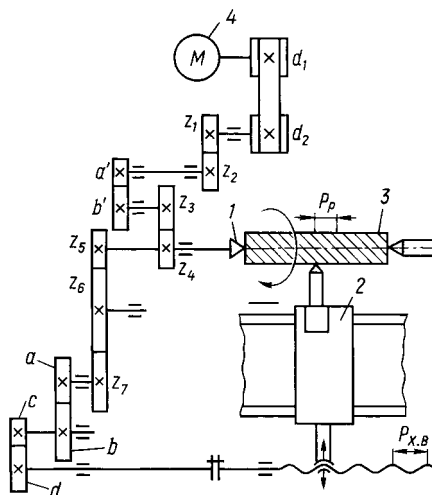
Спрощена кінематична схема токарно-гвинторізного верстата: 1 — шпиндель; 2 — супорт; 3 — деталь, що обробляється; 4 — електродвигун
